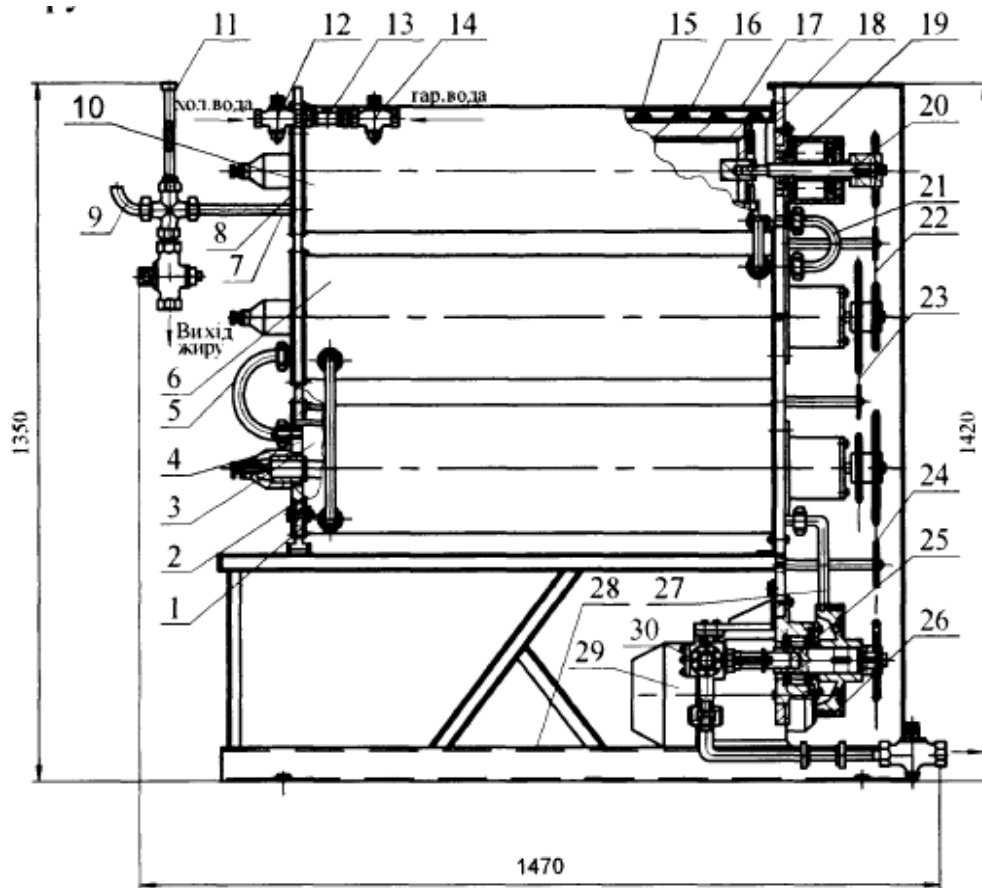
Охолоджувач жиру Д5-ФОЖ: 1, 6, 10 – робочі циліндри; 2 – прокладка; 3 – барабан-витискувач; 4 – кришка; 5, 21 – перехідні патрубки; 7 – вихідний патрубок; 8, 18 – передня і задня стінки циліндра; 9 – патрубок для повернення жиру; 11 – термометр; 12, 14 – вентилі для холодної та гарячої води; 13 – трійник; 15 – металева спіраль; 16 – гумова стрічка; 17 – кожух; 19 – підшипник; 20 – приводний вал; 22, 23, 24 – ланцюгові передачі; 25 – проміжний вал; 26 – клинопасова передача; 27 – нагнітальна труба; 28 – станина; 29 – електродвигун; 30 – насос
